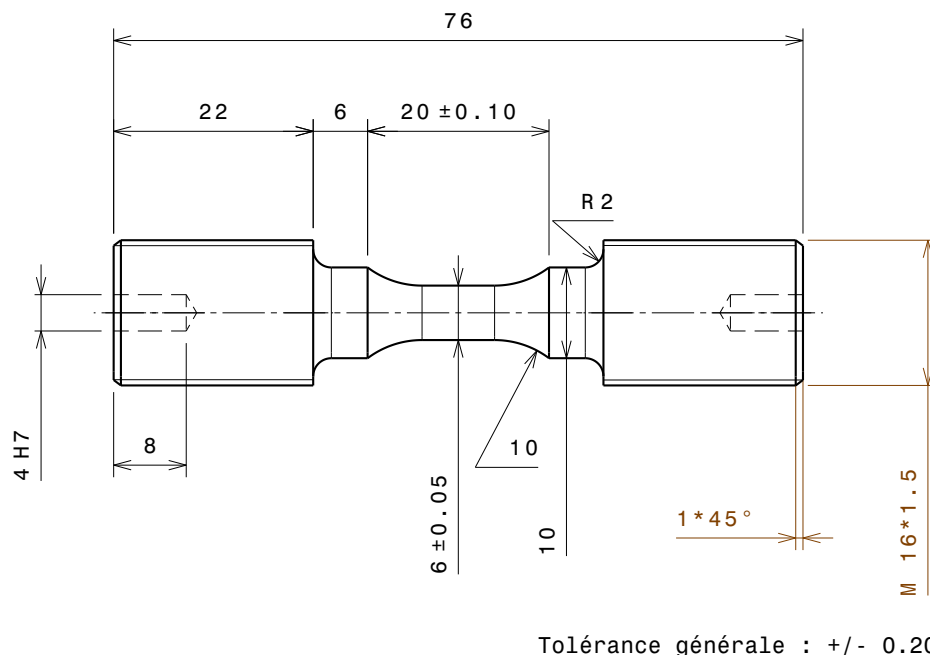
Géométrie des éprouvettes de traction et de fatigue
